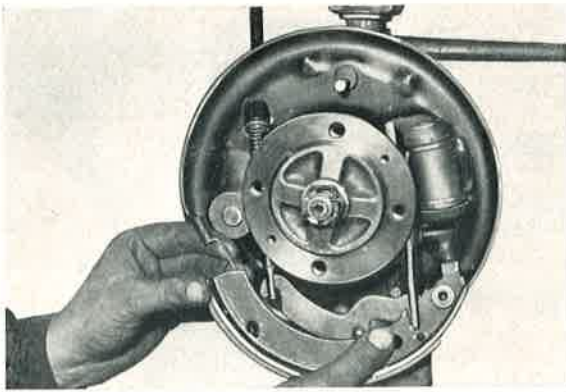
/1: Beim Wiedereinbau d. Bremsbacken wird zuerst mit d. unteren Bremsbacke begonnen. Handbremsseil, beide Zugfedern u. d. Druckstange zuvor einhängen.
